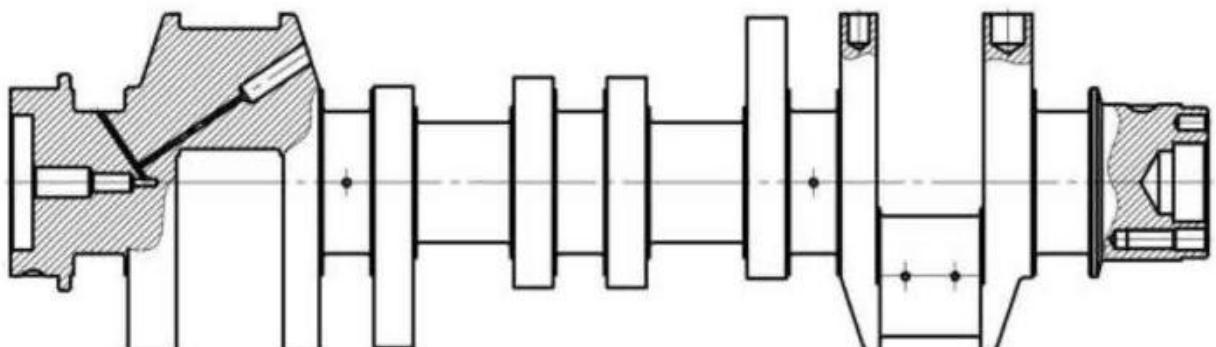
Коленчатый вал в сборе КамАЗ – 740.
